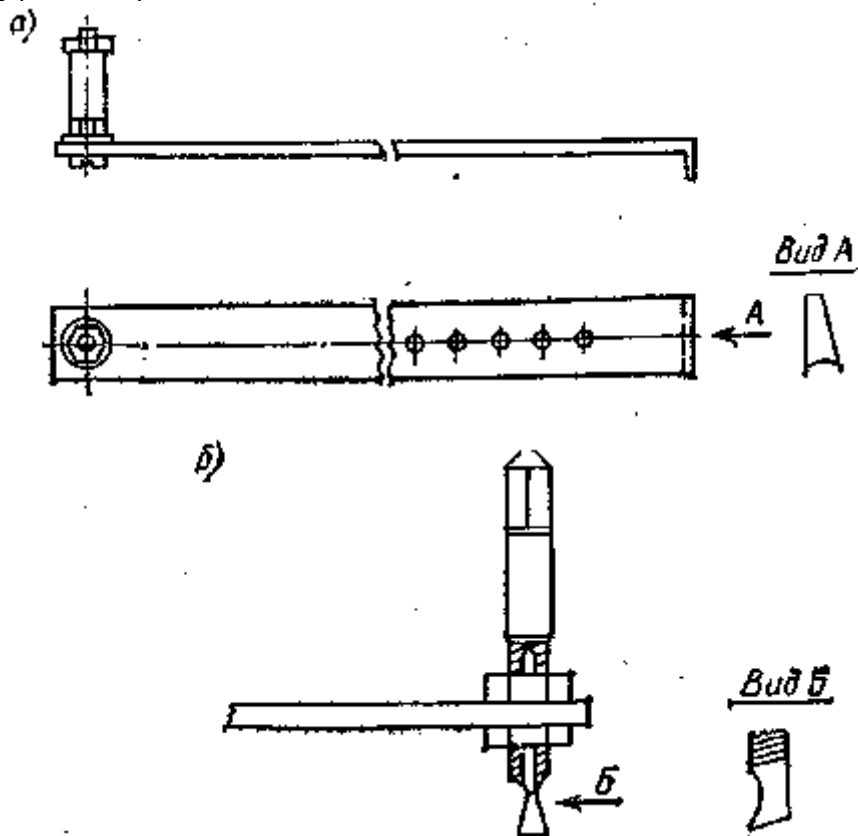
Резак для прорезания круглых отверстий: а — из ножовочного полотна; б — из метчика
